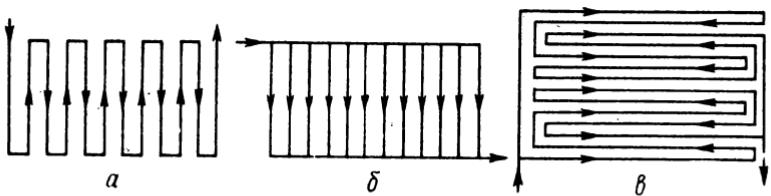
Схемы расположения каналов в нагревательных плитах пресса (а—с)
